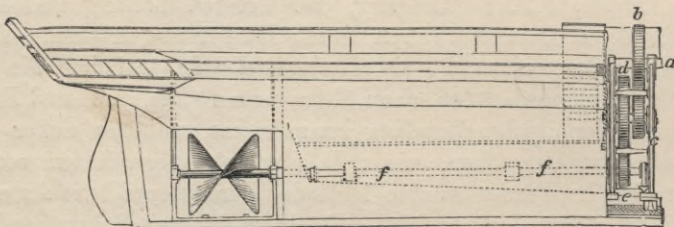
Schiffsschraube des „Archimedes“. 1839.
